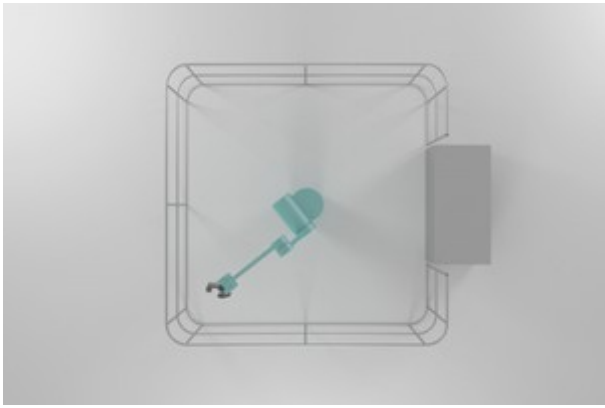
Draufsicht auf den Industrieroboter mit Schutzzaun und Zuführbereich für Werkstücke
